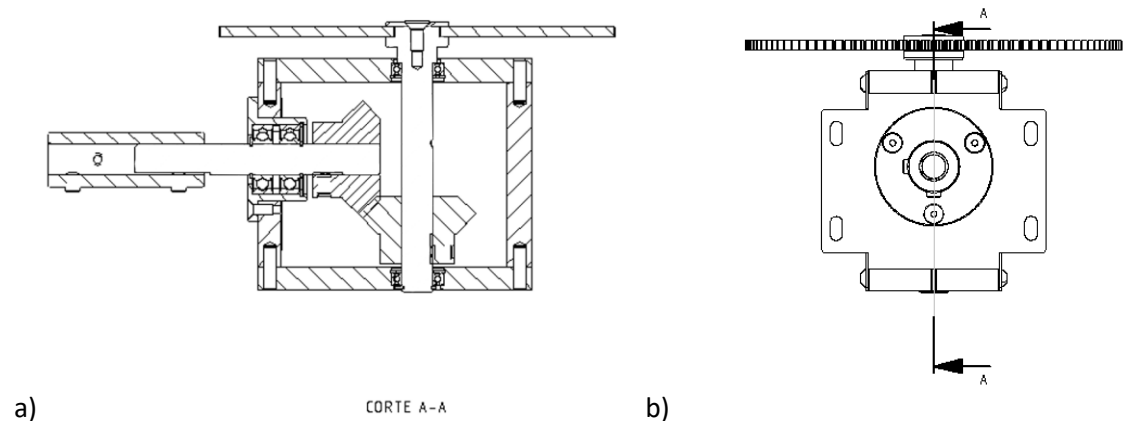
Vista em corte do sistema de transmissão: a) vista em corte; b) vista primária
